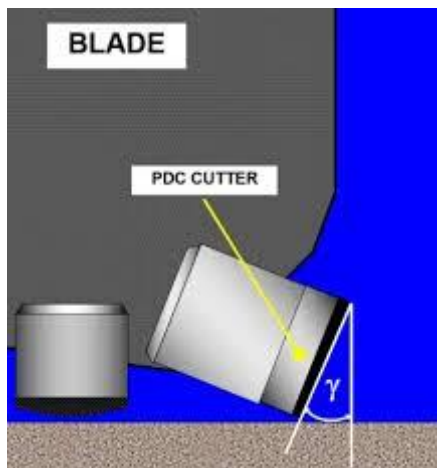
Angle de coupe arrière (Back-rake Angle) [38].
